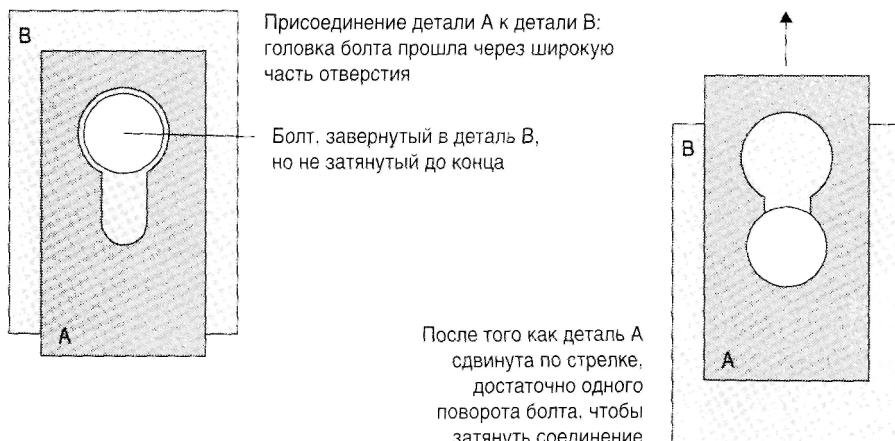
Отверстия грушевидной формы допускают быструю разборку и сборку болтовых креплений
